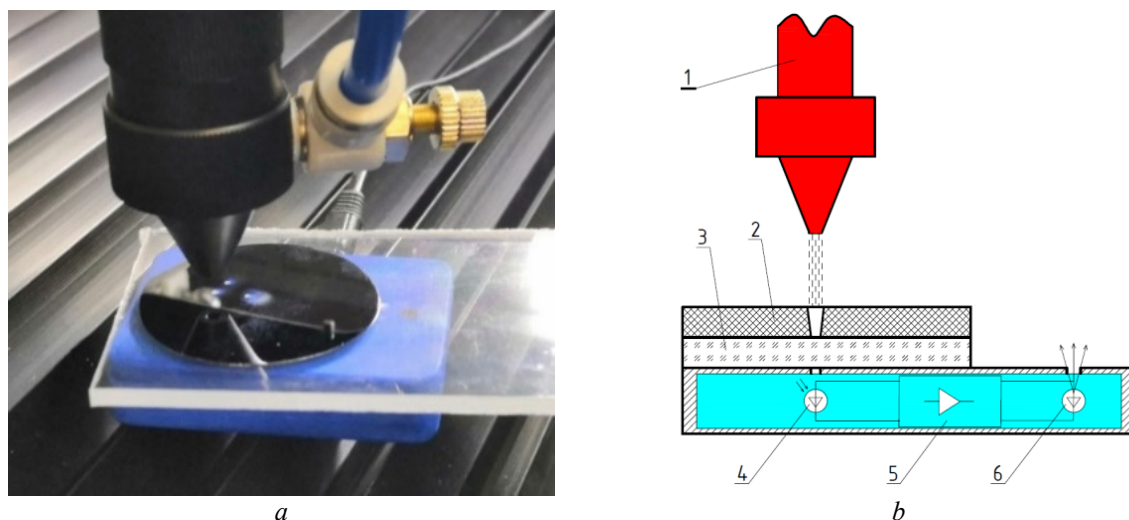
Внешний вид (а) и схема (b) лазерной прошивки отверстий: 1 – лазер; 2 – кремниевая подложка; 3 – плексиглас; 4 – фотодиод; 5 – модуль усилителя; 6 – светодиод
